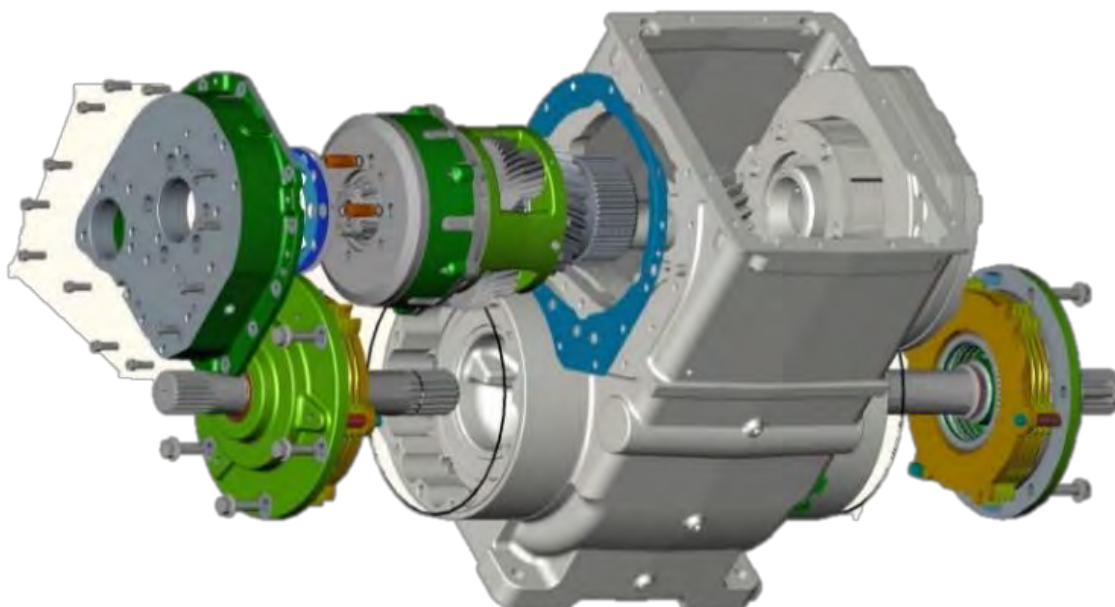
"Explosionado del proceso de montaje de la estación 3"
